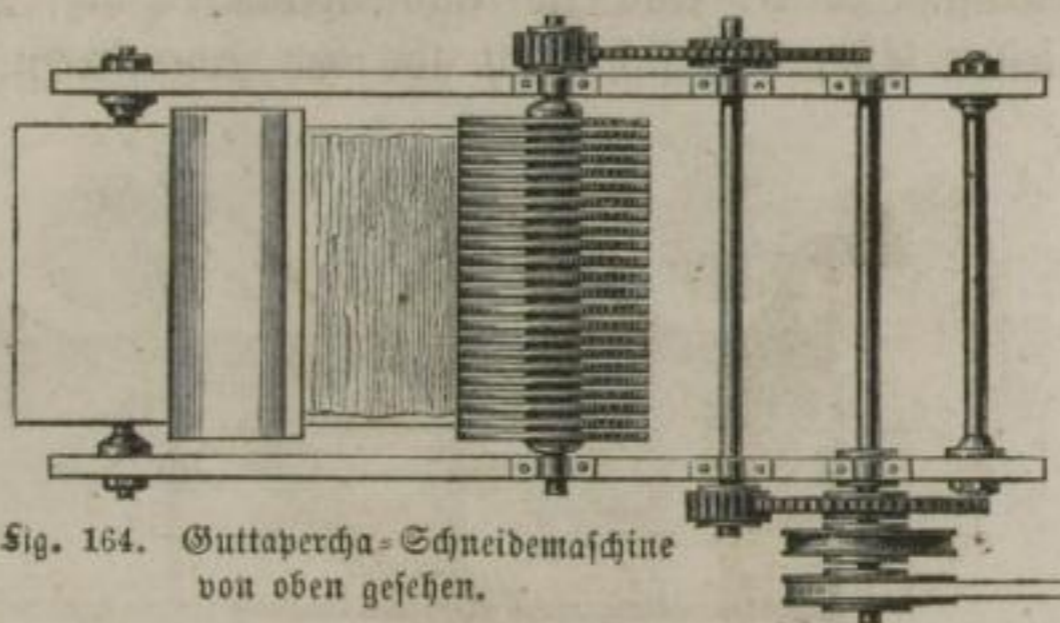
Guttapercha-Schneidemaschine von oben gesehen.
